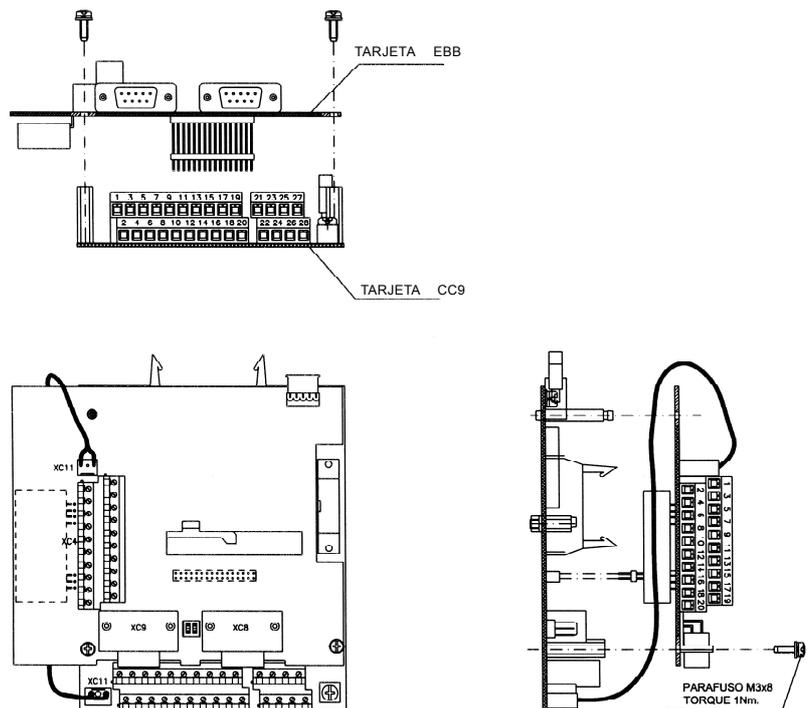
Posición de los elementos de ajuste - tarjeta EBB
